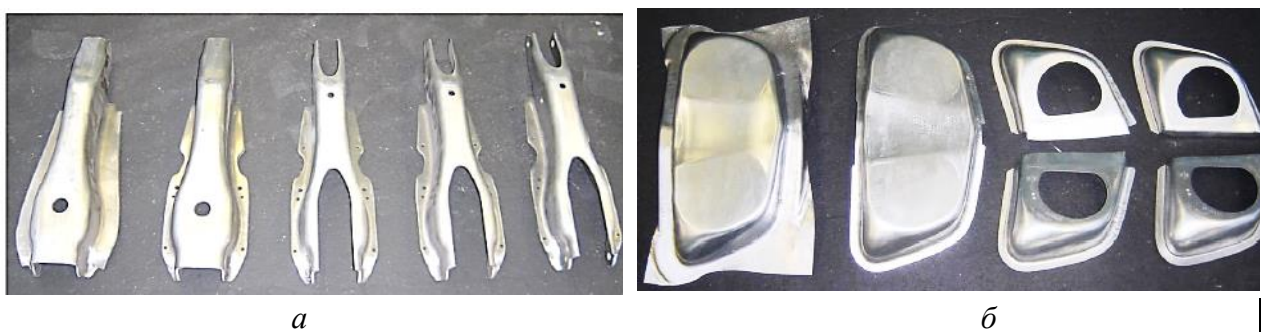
Детали из алюминиевых сплавов, полученные штамповкой:
